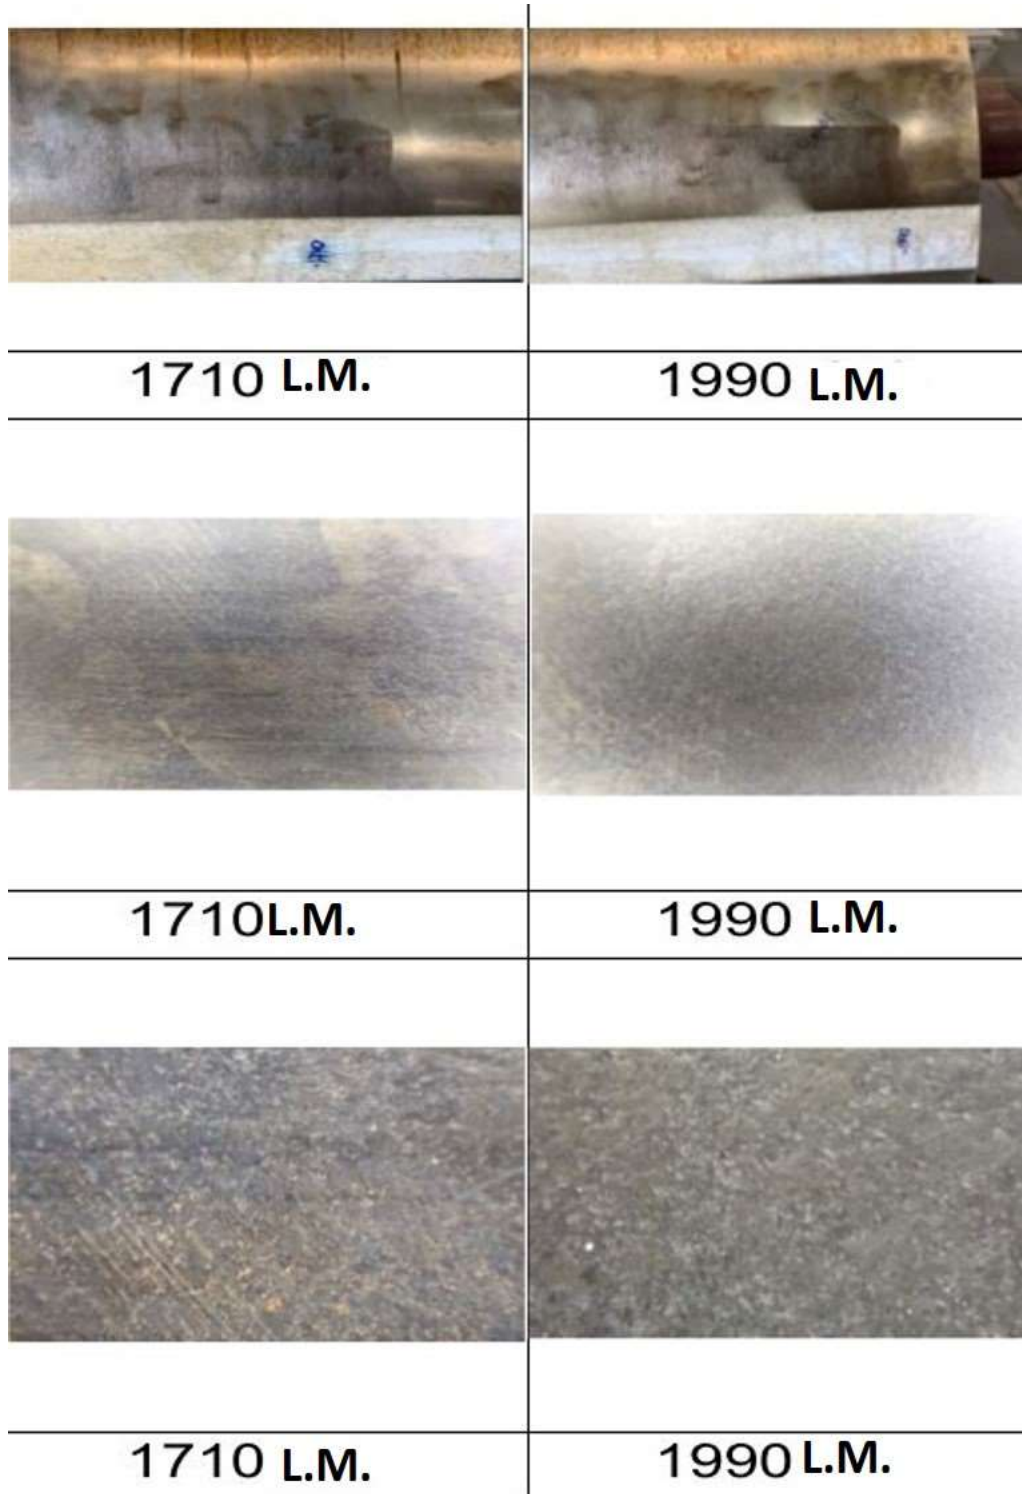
Foto em zoom lado motor. Fonte: Autor
